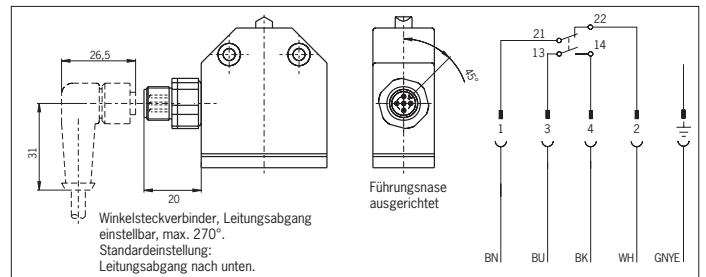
Maßzeichnung/Anschlussplan SN01.558SVM5 mit Steckverbinder M12 (SVM5, 5-polig)
